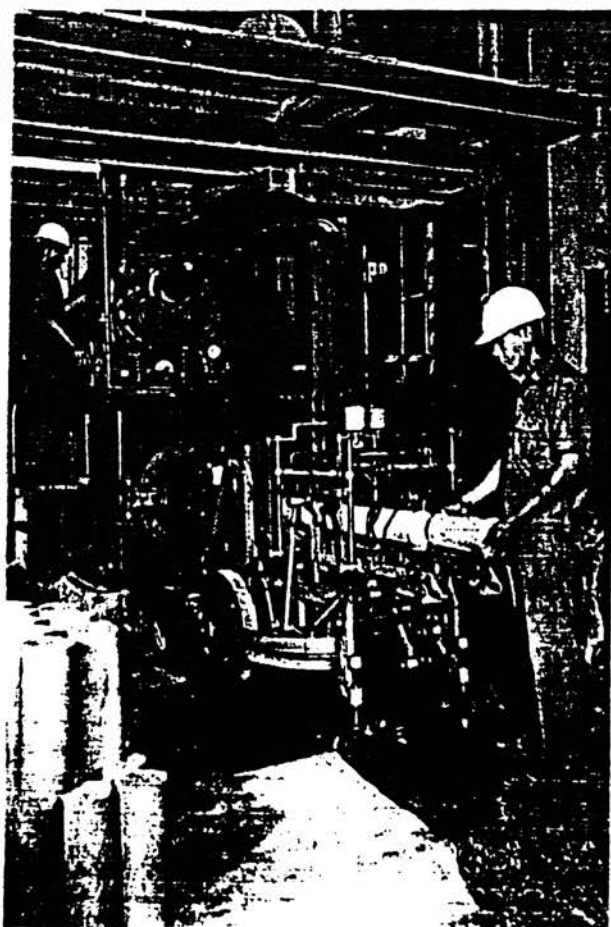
การขึ้นรูปด้วยเครื่อง Impact Press, Toggle Press, Vacuum Extruder และ Runner Brick Press
